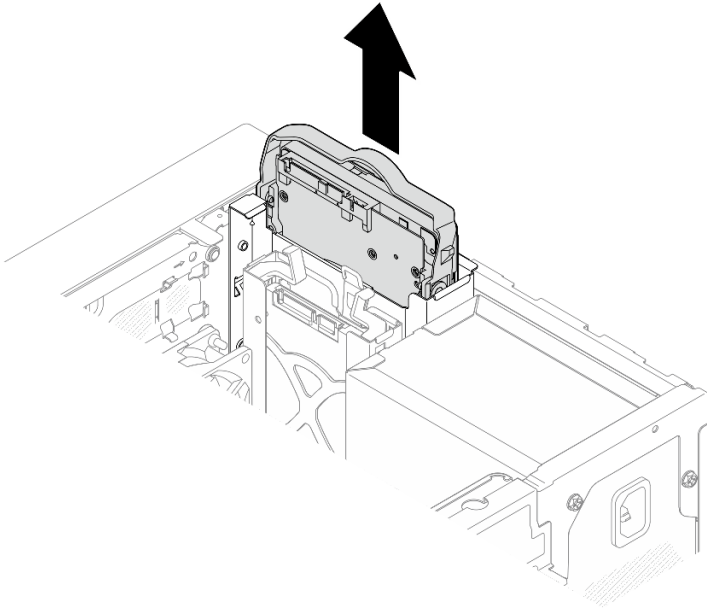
Entfernen einer Laufwerkbaugruppe aus Laufwerkposition 0
